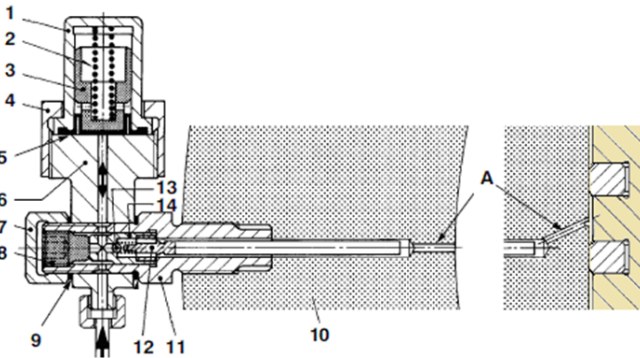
Складові лубрикаторної системи двигунів РГА: 1-кришка акумулятора; 2-пружина; 3-поршень; 4-накидна гайка; 5-мембрана; 6-корпус акумулятора; 7-гайка штуцера; 8-заглушка; 9-прокладка; 10-циліндрова втулка; 11-корпус штуцера; 12-стрижень; 13-кульковий клапан; 14-пружина клапана.
